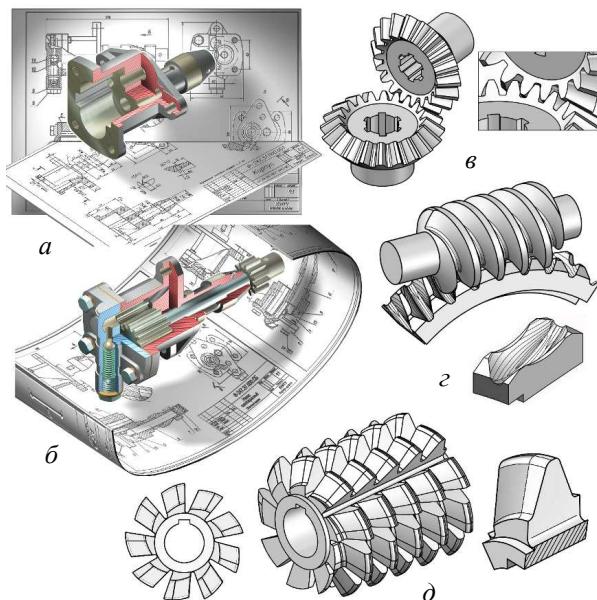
К темам «Фотореалистичность» и «Геометрически точные модели»: а – фотореалистичное изображение корпусной детали; б – фотореалистичное изображение узла; в – коническая передача; г – червячная передача; д – червячная модульная фреза
